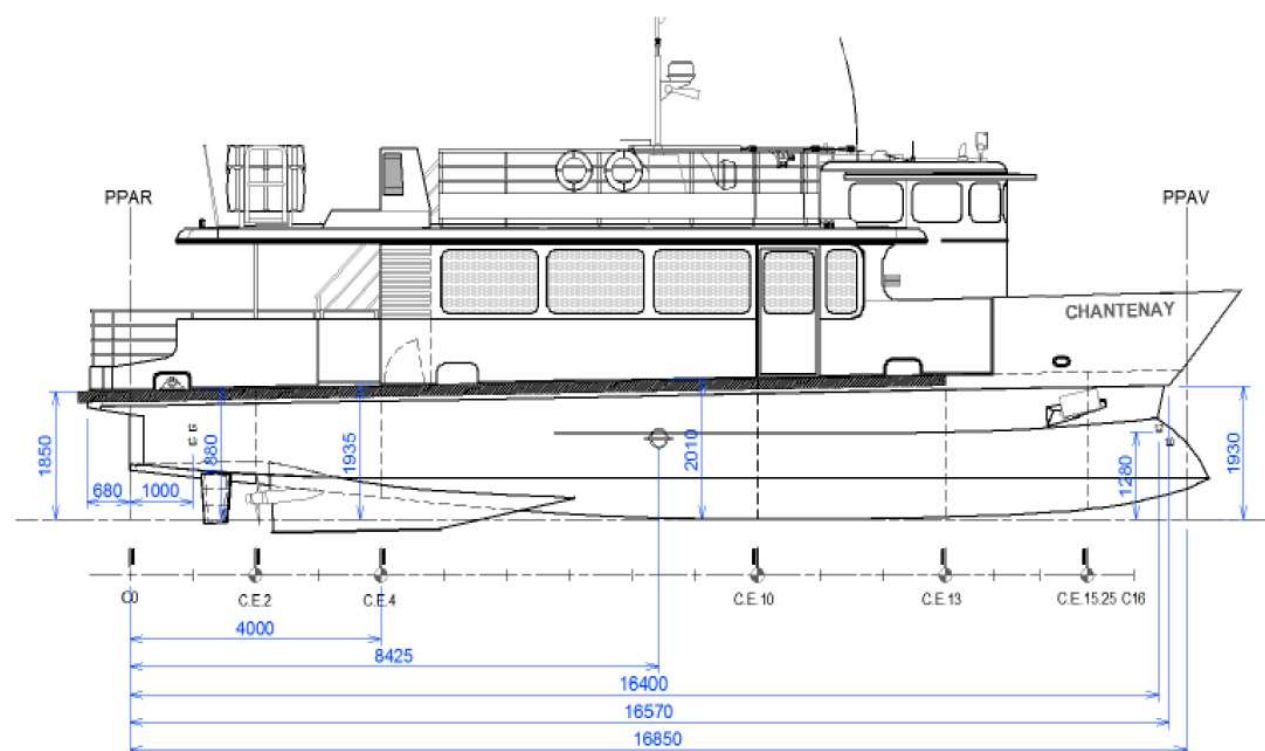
Plan d'un navire type (SCE, décembre 2023)
